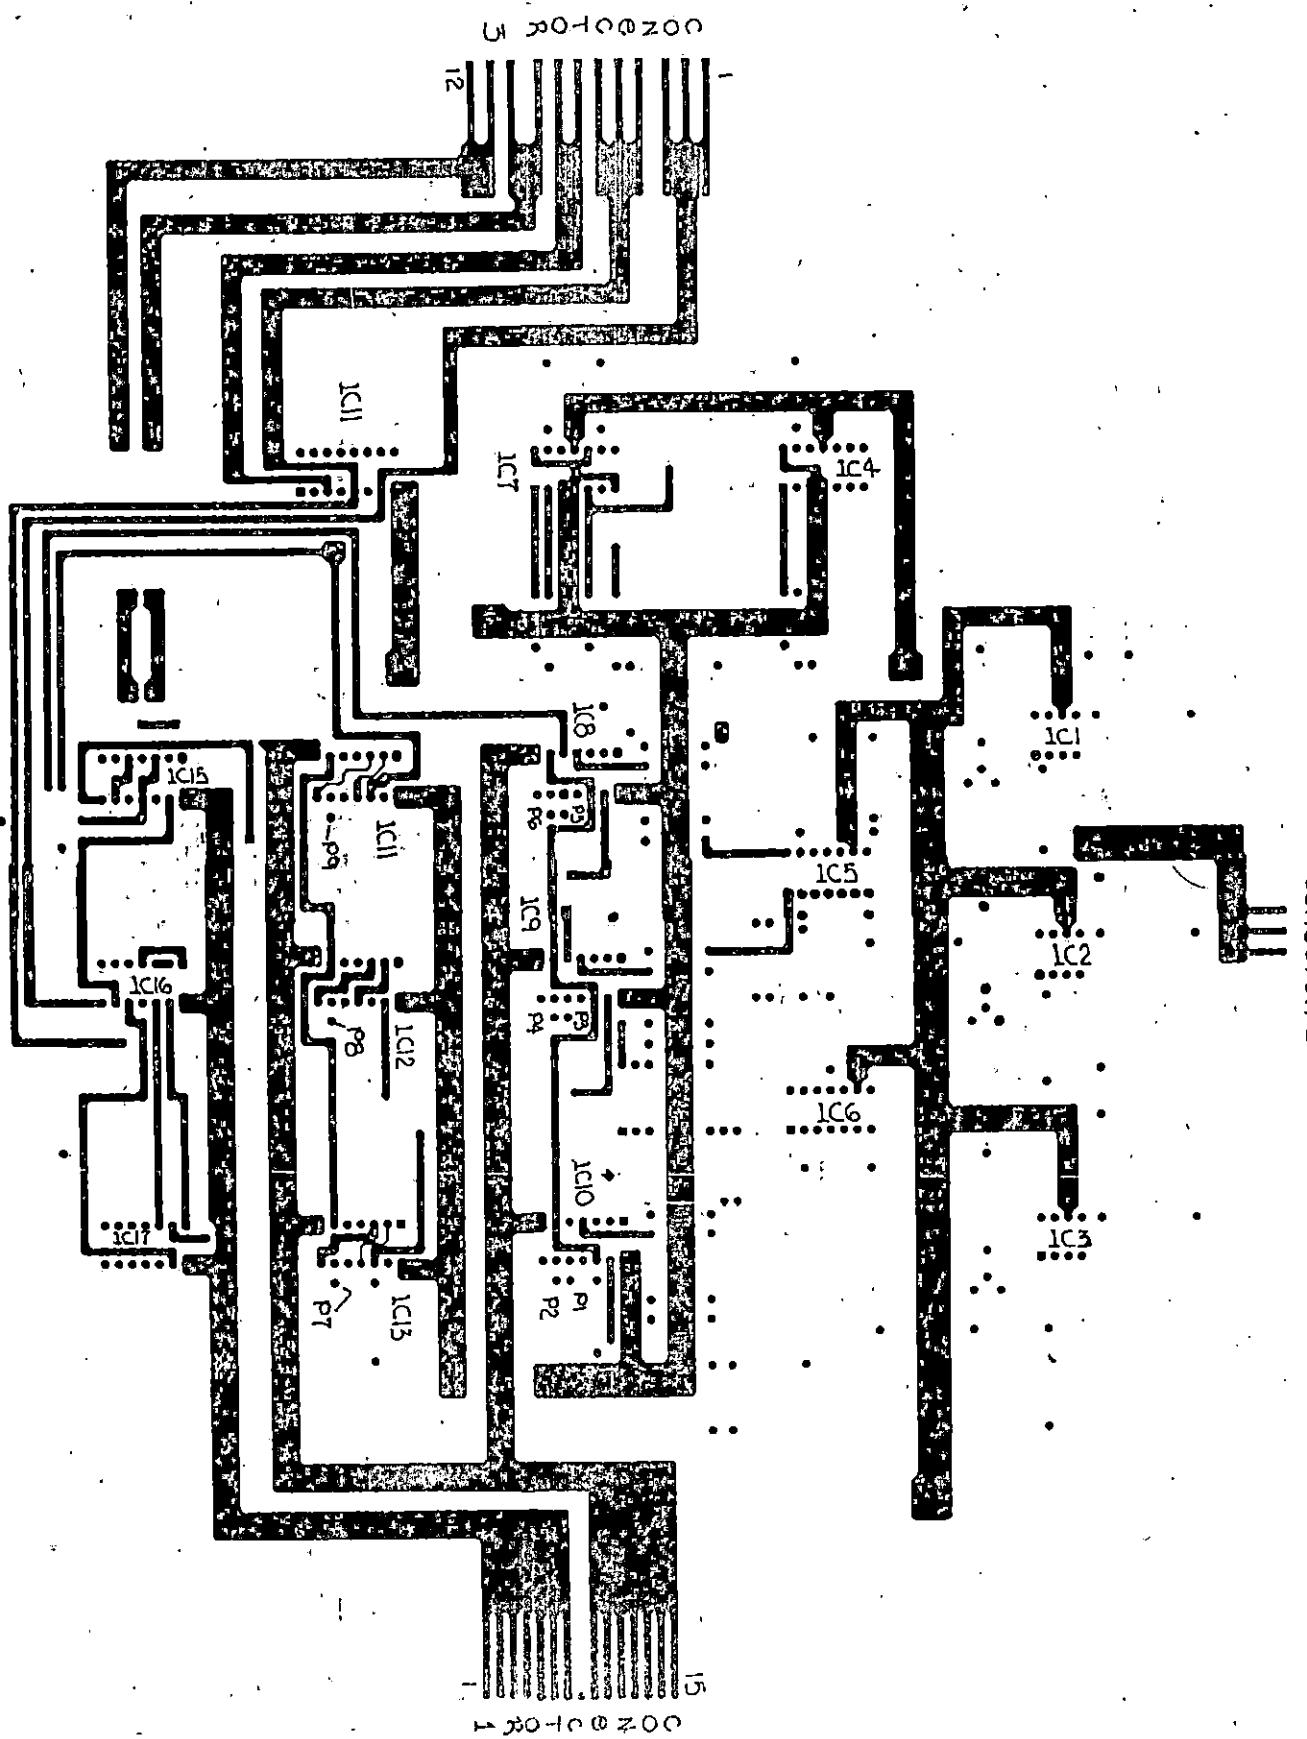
Lado Soldadura de la Tableta que controla un grupo de tres alumnos.
